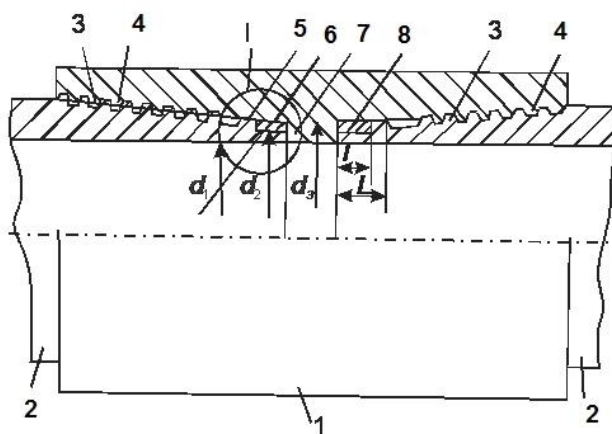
Схема з'єднання обсадних труб з різьбою ОТТГ: 1 - муфта, 2 - труба, 3 - різьба на трубі, 4 - різьба на муфті, 5 - за різьбова канавка, 6, 8 - герметизуючий елемент, 7 - циліндрична частина муфти
